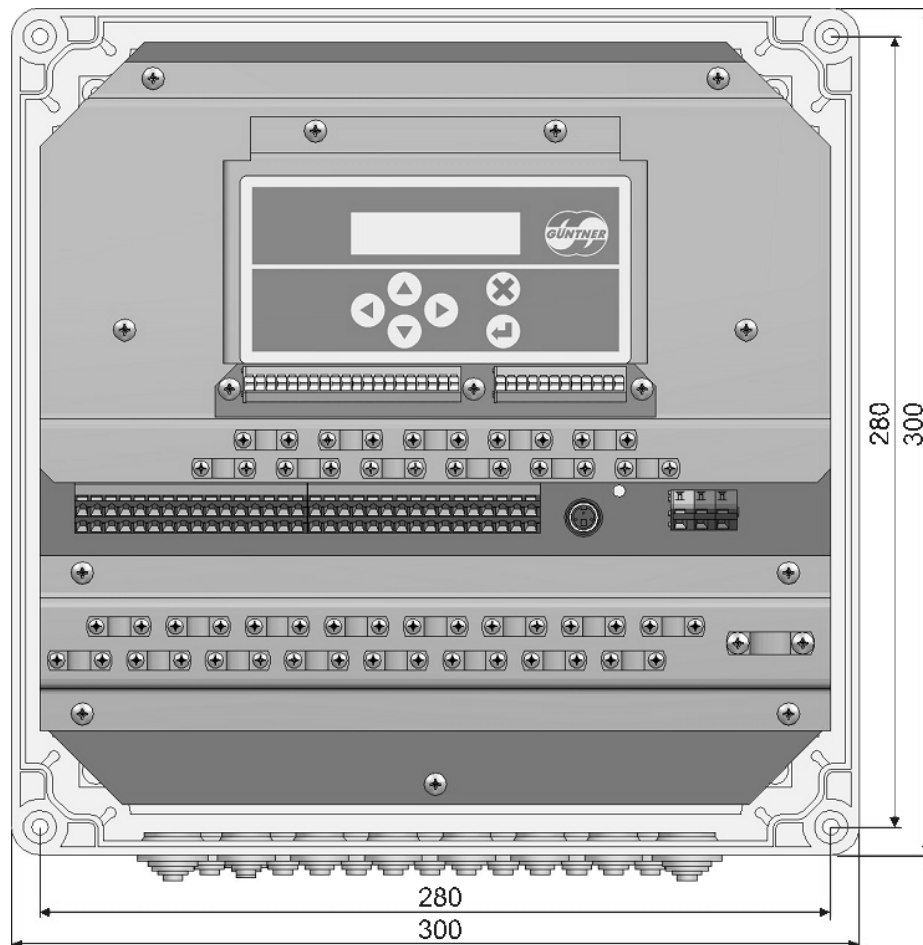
Dimensões de caixa GMM EC 16 (.1)
